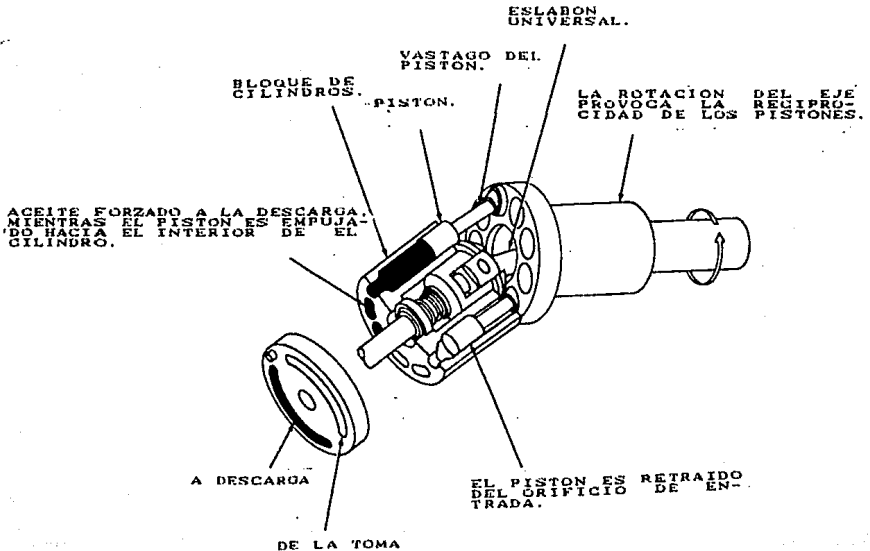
BOMBA DE PISTON AXIAL.
